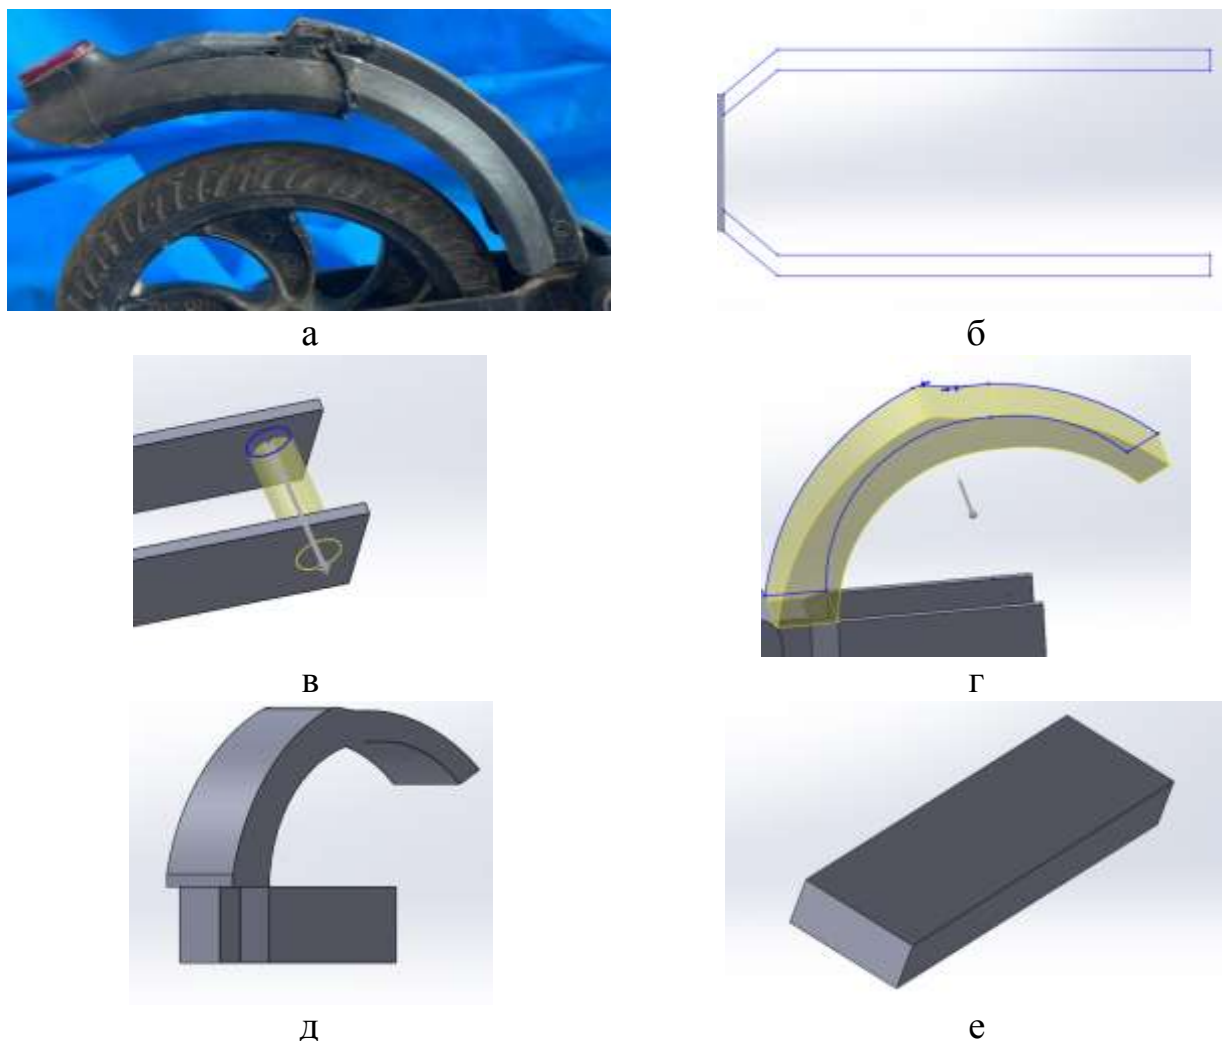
Заднее крыло и аккумулятор; а – реальный вид заднего крыла; б – эскиз вилки; в – вал крепления ведомого колеса; г – эскиз и вытяжка заднего крыла; д – 3D-модель заднего крыла и вилки е – 3D-модель аккумулятора
